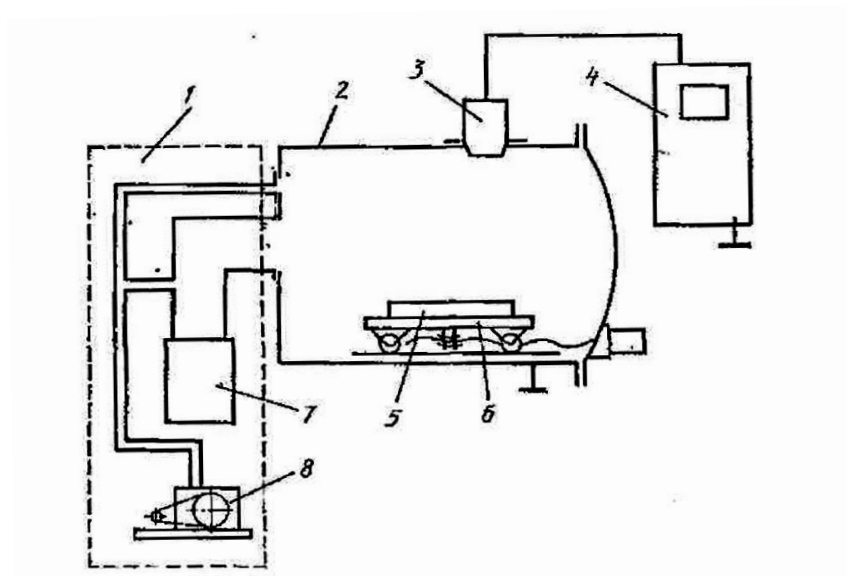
Схема установки для электронно-лучевой сварки: 1 - откачная система; 2 - вакуумная камера; 3 - электронно-лучевая пушка; 4 - высоковольтный источник питания; 5 - заготовка (изделие); 6 - тележка; 7 - диффузионный насос; 8 - форвакуумный насос.
